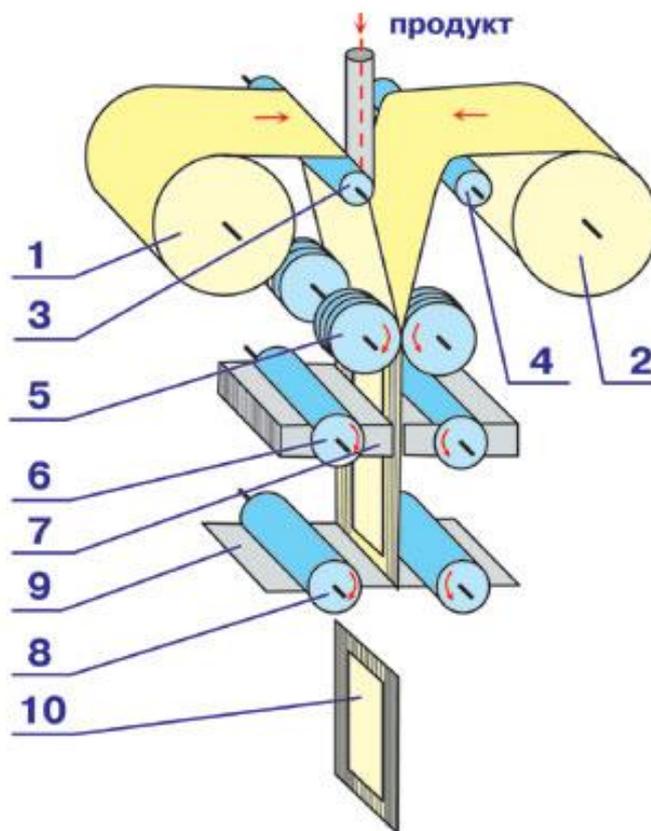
Схема упаковочного аппарата вертикального типа непрерывного действия, образующей плоский пакет наложением полос с двух рулонов
